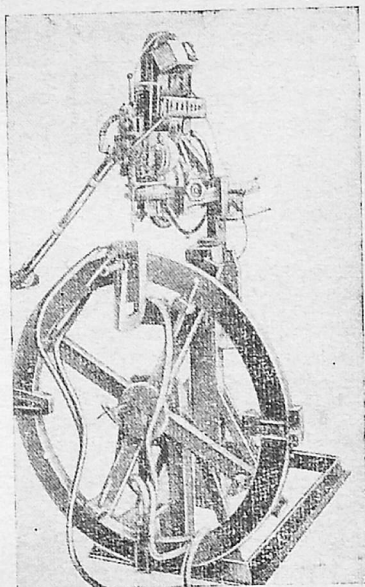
Установка для электрошлаковой сварки фланцев.
